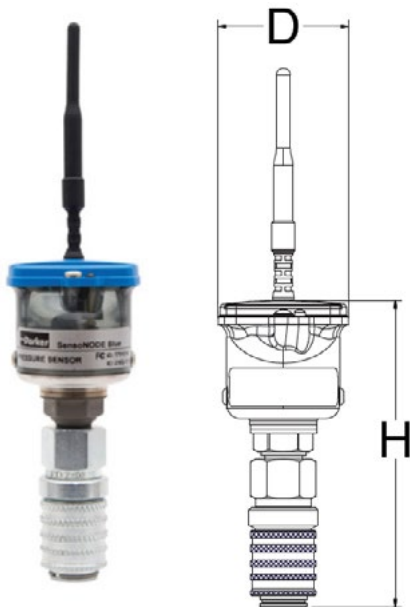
Disegno dimensionale SNPT4-xxx-B-4MO
